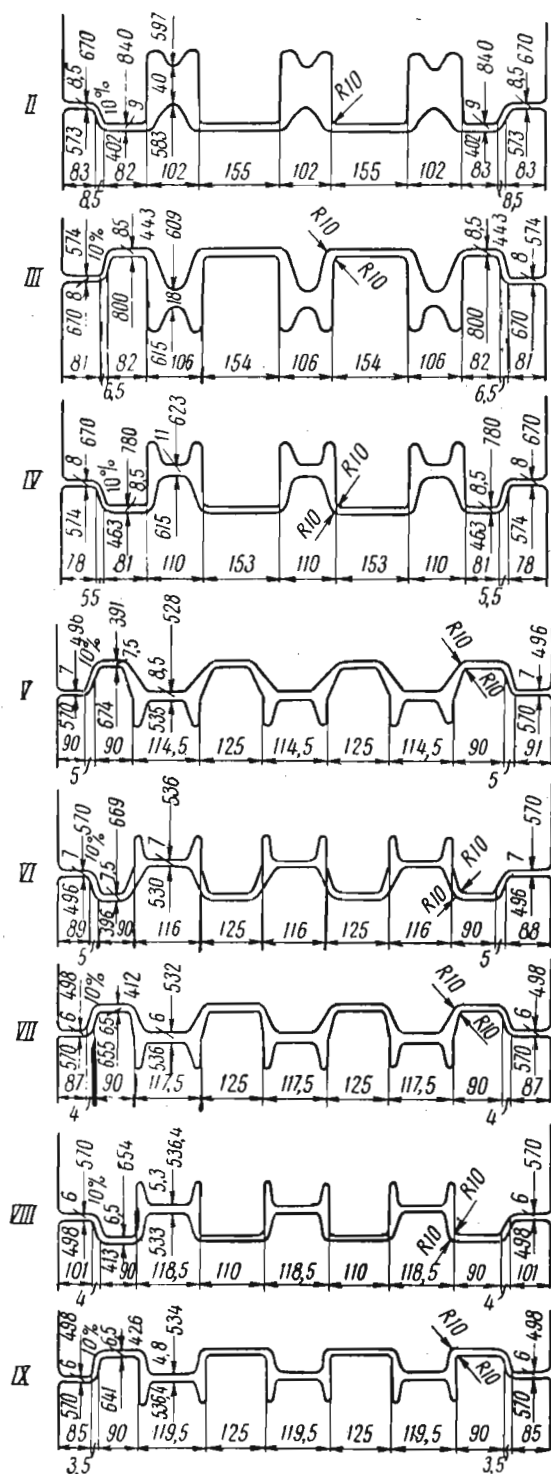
Калибровка валков стана 500 для прокатки двуглавой балки № 12:
